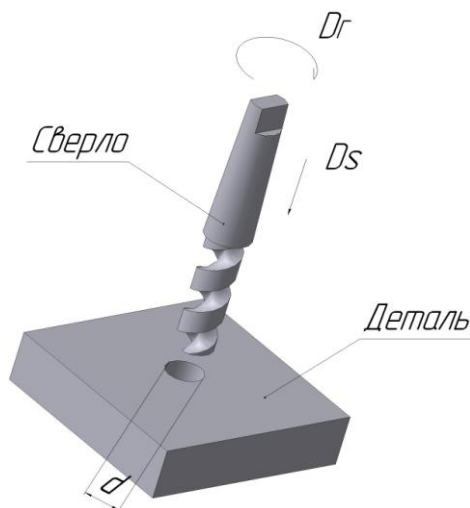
Схема обработки отверстия (сверление): d – диаметр отверстия.
